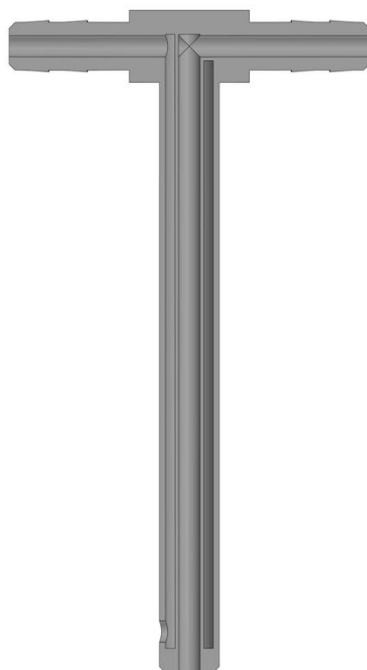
Трубка Пито-Прандтля с плоской поверхностью вокруг отверстия статического напора и фасками, образец II, разрез
